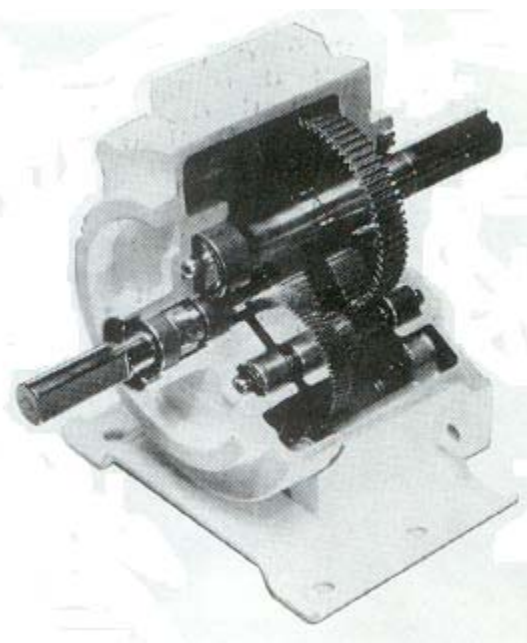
Reductor cilíndrico de dos etapas: la primera es de engranajes de dientes oblicuos y la segunda de engranajes de dientes rectos.
